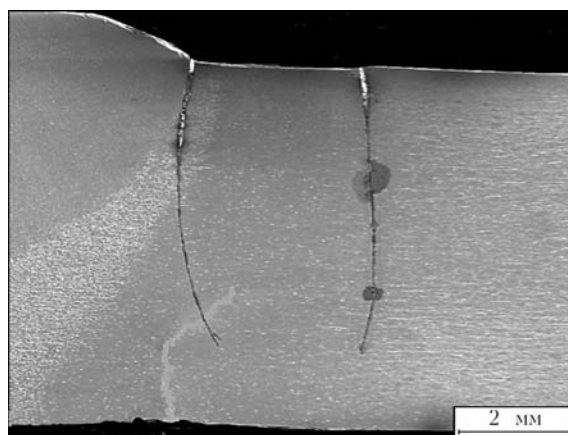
Макрошлиф сварного соединения с трещинами после испытаний
